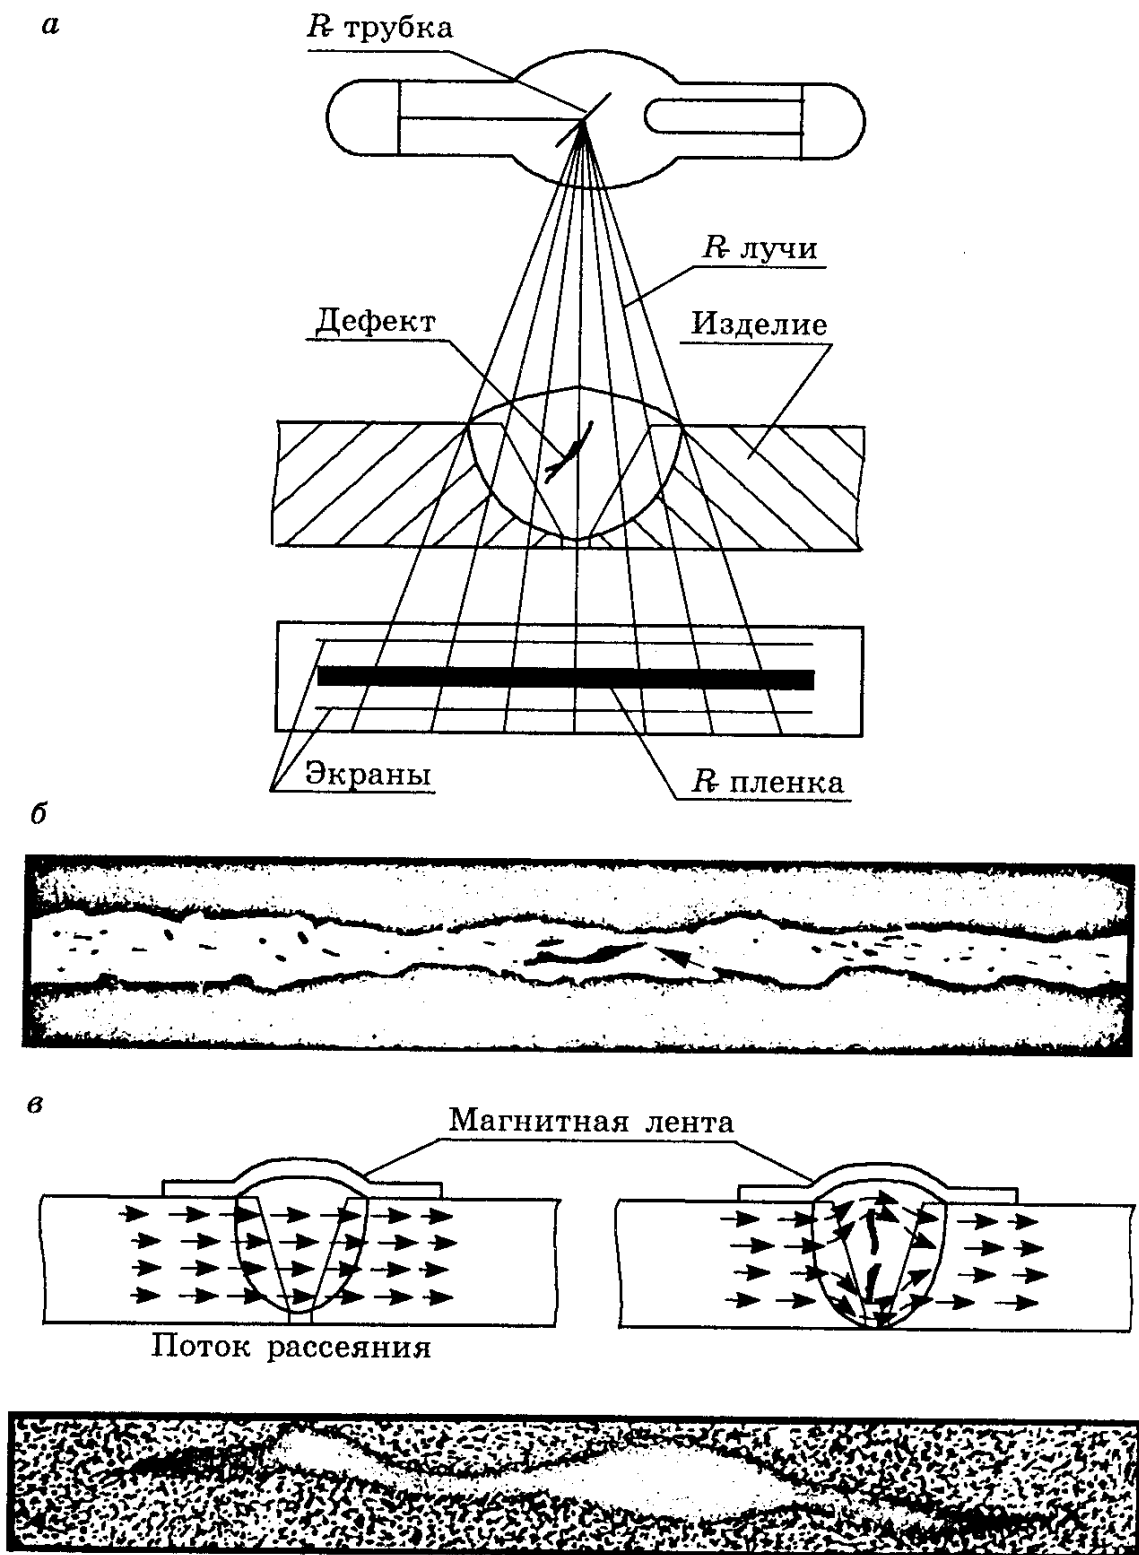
Схема контроля сварного соединения: *a* — просвечиванием рентгеновскими лучами; *б* — рентгенограмма шва; *в* — намагничиванием
